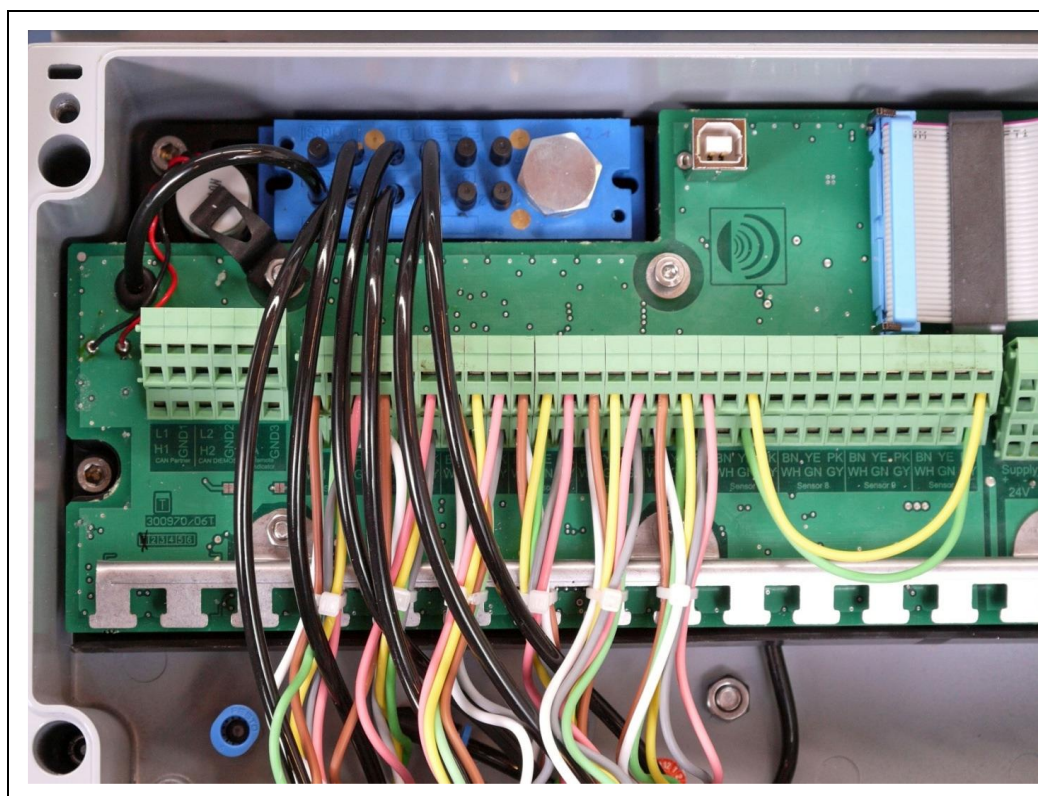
Montage und Installation abgeschlossen (Schritte 1-7; Bsp. mit 6 Hybridschläuchen)
